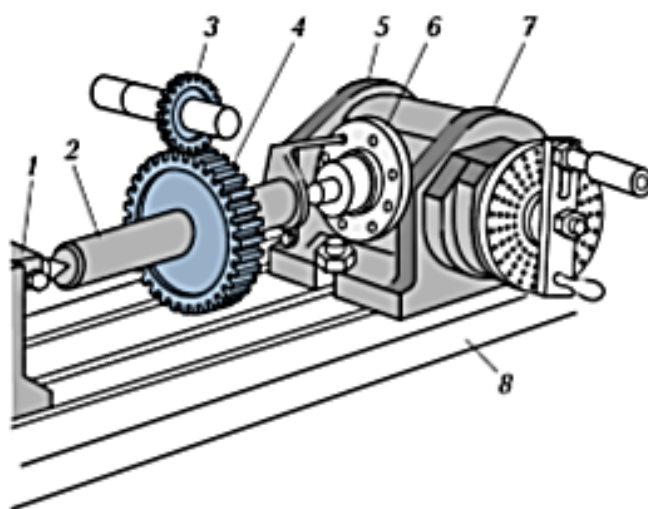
Фрезерование цилиндрического зубчатого колеса дисковой модульной фрезой:
